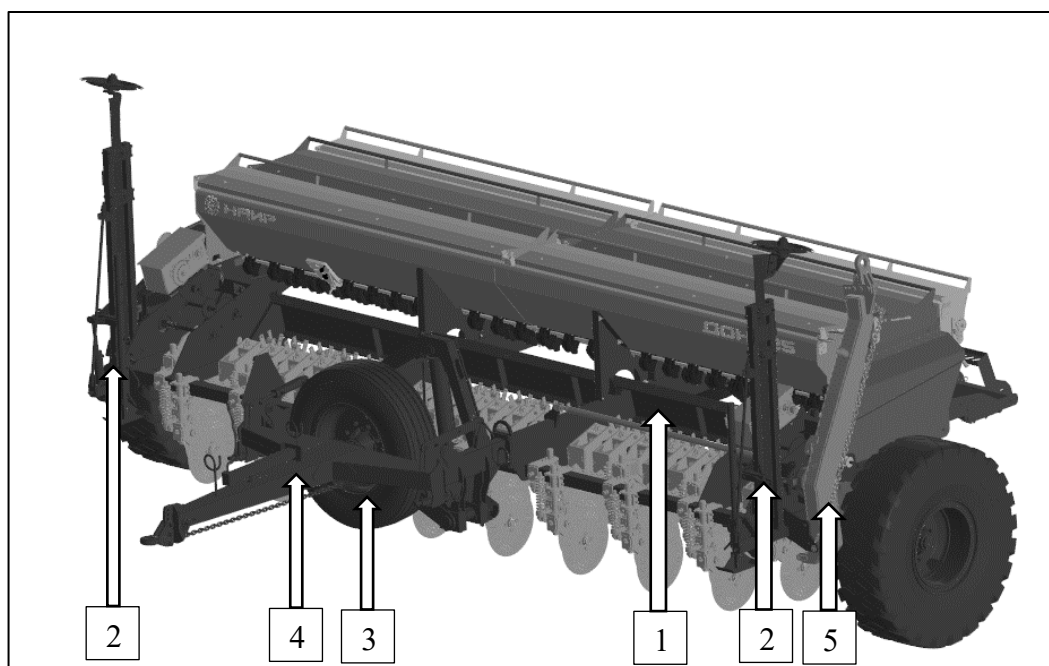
Вид спереди: 1 – рама сеялки; 2 – маркеры; 3 – колесо боковой транспортировки; 4 – центральный фаркоп; 5 – фаркоп механизма боковой транспортировки
